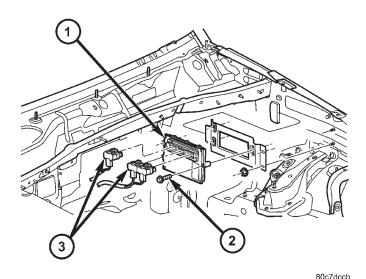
DESMONTAJE E INSTALACION DEL PCM
